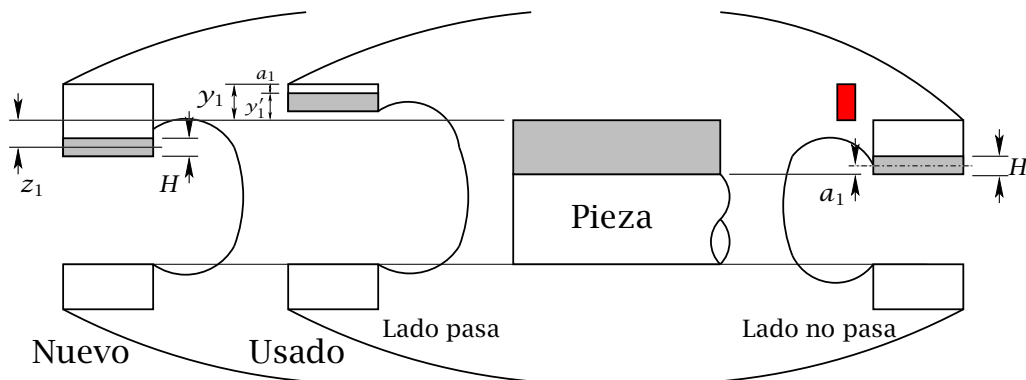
Límites de tolerancia de un calibre de herradura para dimensiones superiores a 180 mm.
